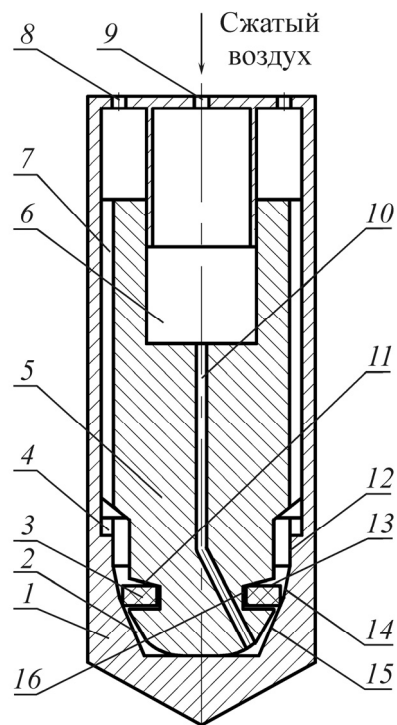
Схема устройства ударного действия с упругим клапаном: 1 — корпус (наковальня); 2 — камера обратного хода; 3 — упругий кольцевой клапан (упругое кольцо); 4 — пазы ограничителя обратного хода; 5 — ударник; 6 — камера прямого хода; 7 — продольные пазы; 8 — выпускное отверстие; 9 — впускное отверстие; 10 — канал; 11 — коническая поверхность задней стенки кольцевой канавки; 12 — цилиндрическая поверхность; 13 — торцевая поверхность упругого кольцевого клапана; 14 — дополнительная коническая поверхность; 15 — конический выступ; 16 — кольцевая канавка
